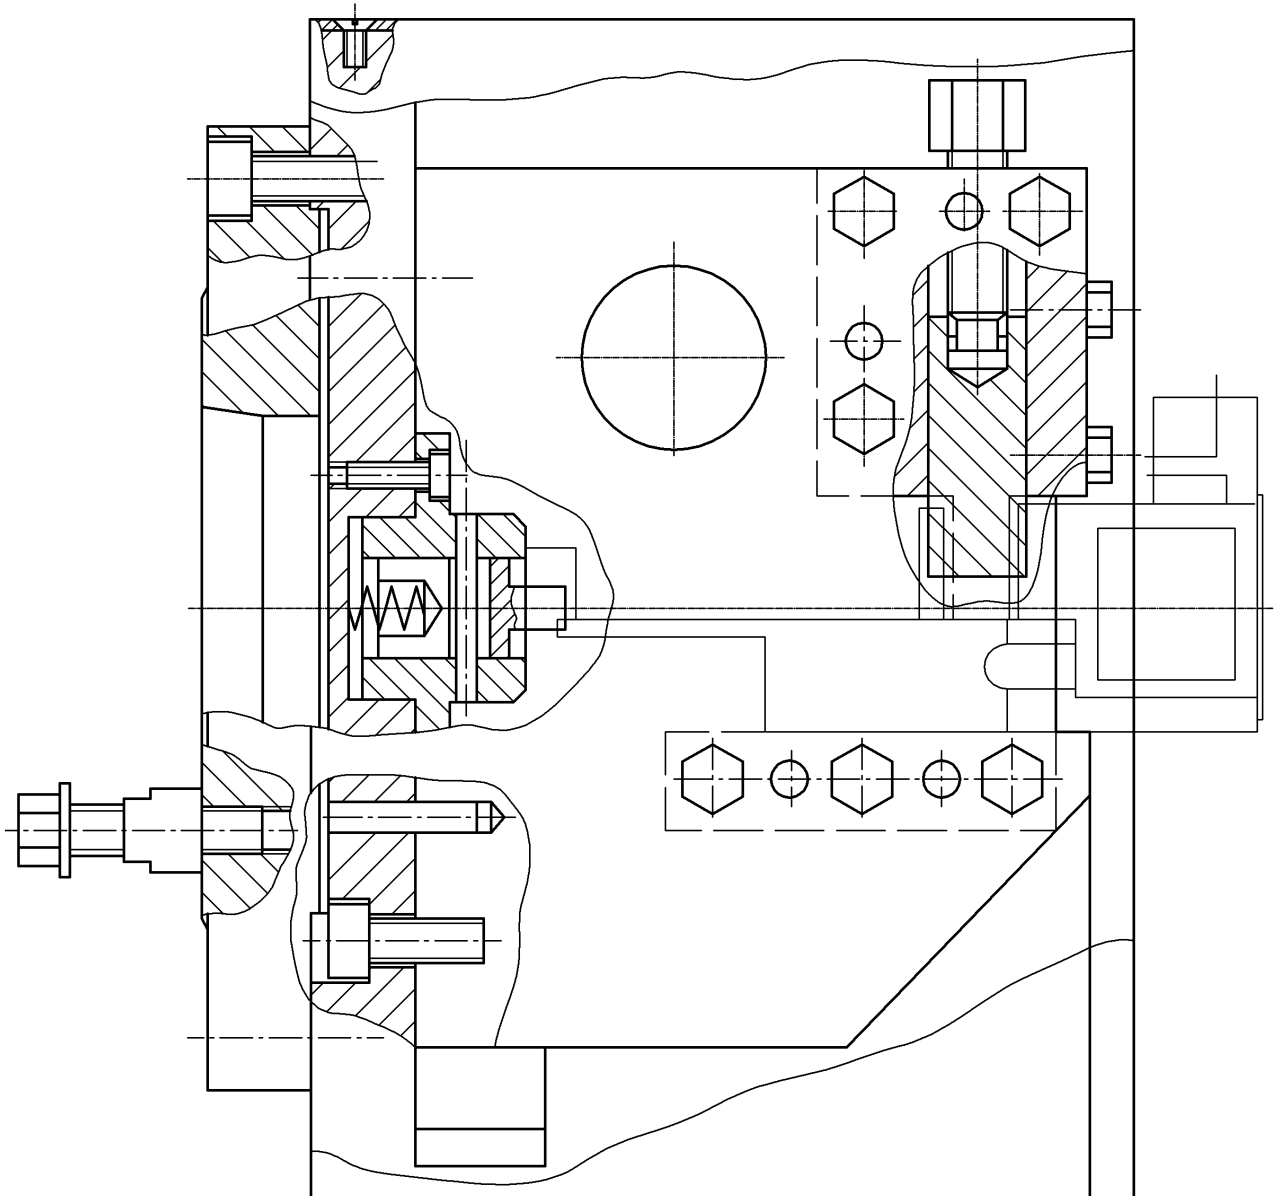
Пристрій для токарного оброблення корпусу
